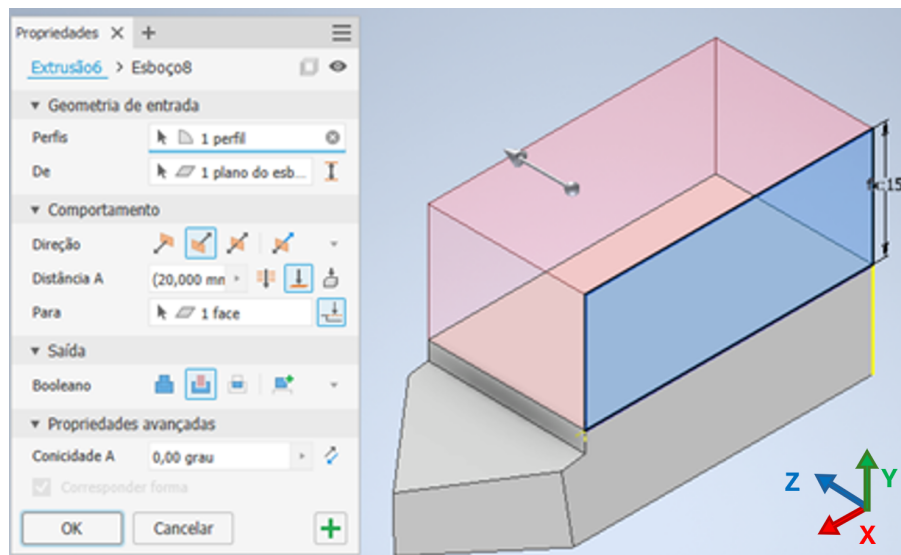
Aplicação da Extrusão 6 sobre o Esboço 8 e seus parâmetros
